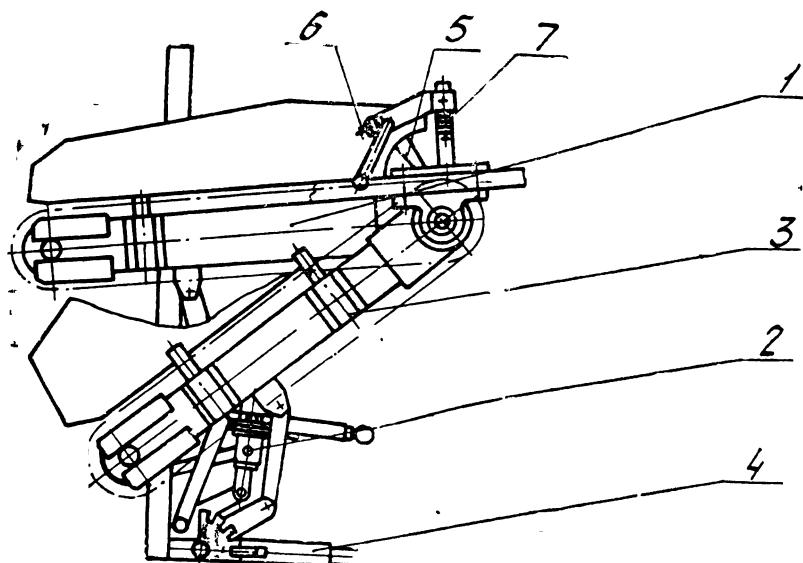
Регулировка расположения основной и дополнительной горок:
